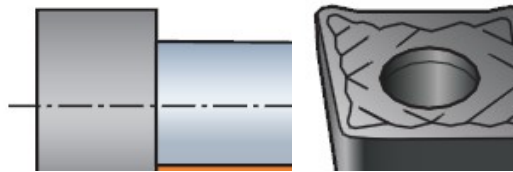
Інструмент для напівчистої та чистої обробки зовнішньої поверхні та підрізування торця
